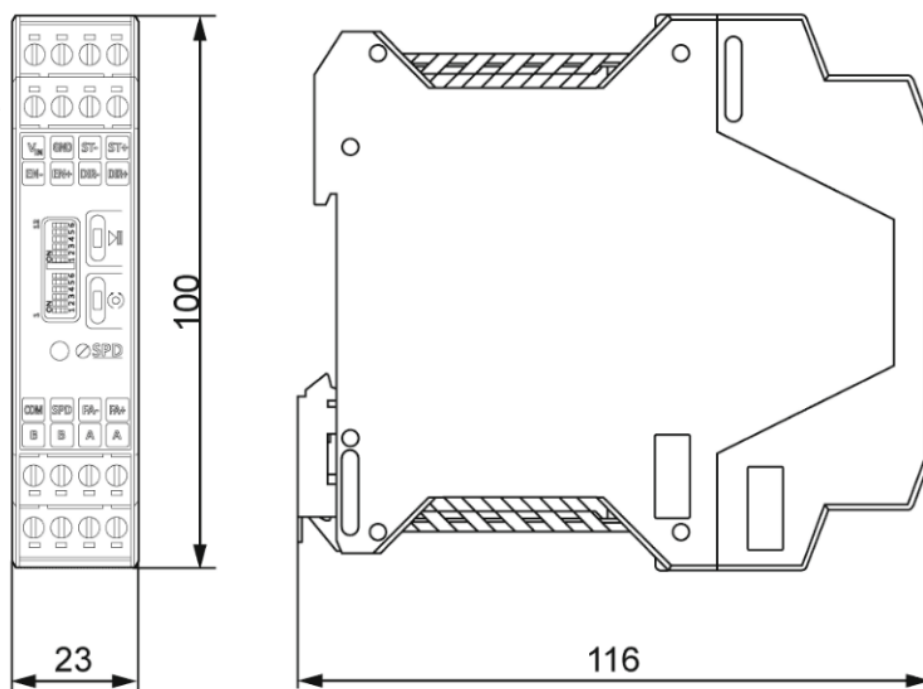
Dimensioni del driver motore passo-passo RS 206412
